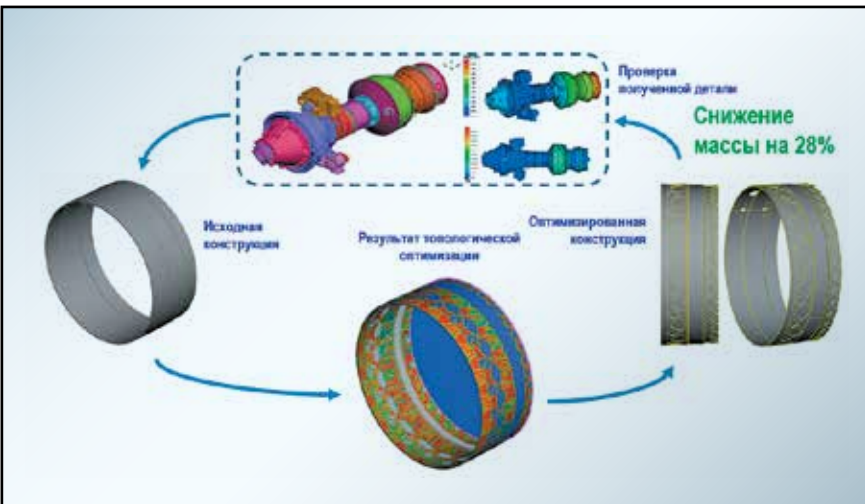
Схема процесса оптимизации обечайки корпуса компрессора
